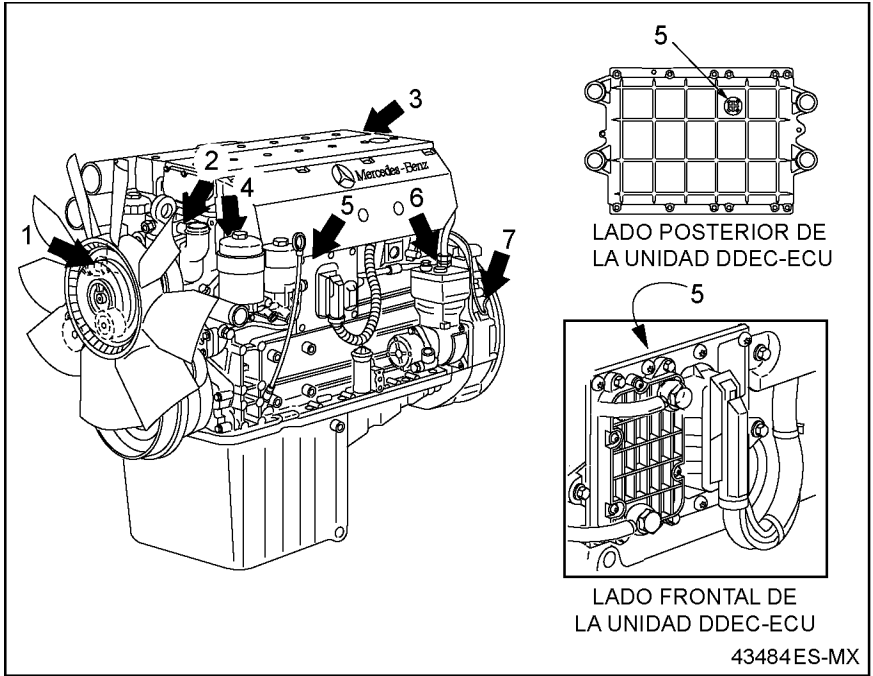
Localización del Sensor en el Lado Izquierdo del Motor de MBE 900 EGR.
